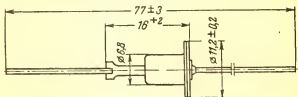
Габаритный чертеж диодов Д7Б—Д7Ж.
